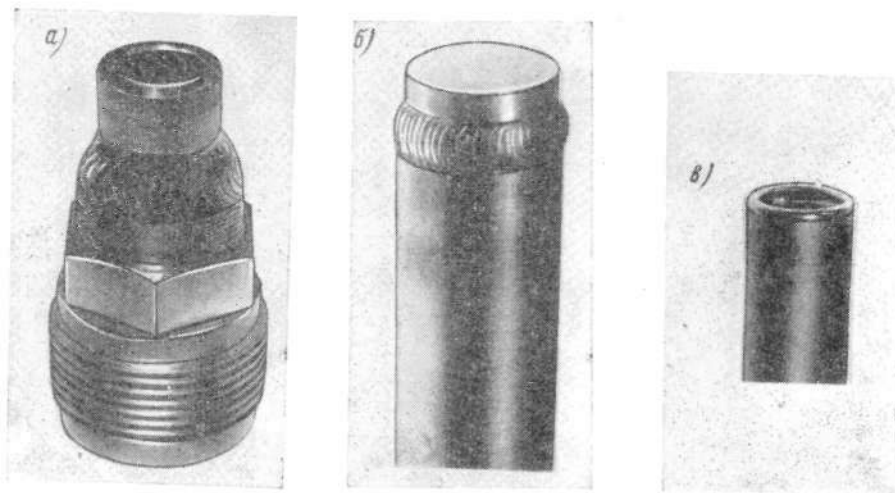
Внешний вид швов на соединениях труб с концевой арматурой: а — со штуцером; б, в — с заглушкой.
